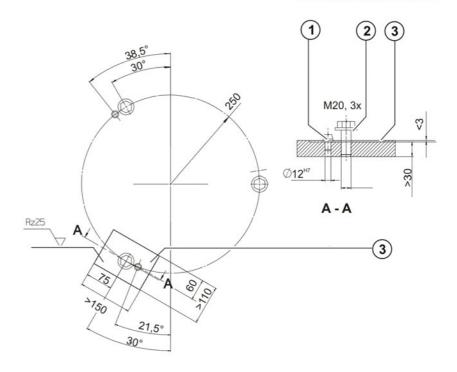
Fixação em suporte de máquina, desenho dimensional
